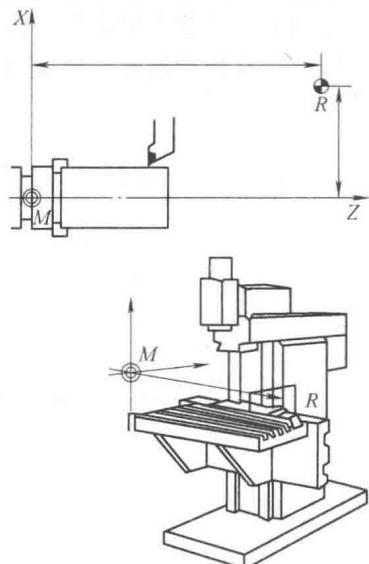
数控车床和立式数控铣床的机床原点及参考点
